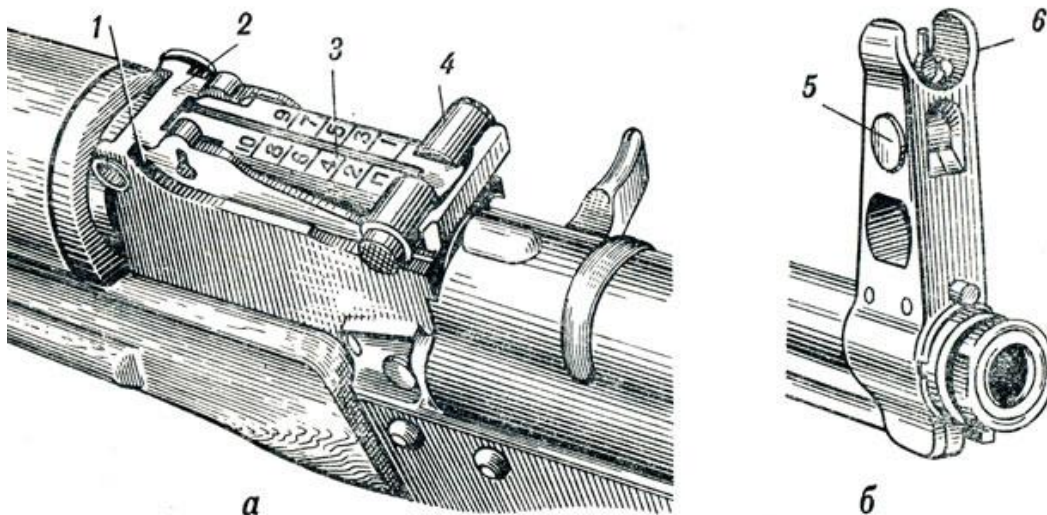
Прицельное приспособление: а - прицел; б - основание мушки; 1 - колодка прицела; 2 - пластинчатая пружина; 3 - прицельная планка; 4 - хомутик; 5 - полозок с мушкой; 6 - предохранитель мушки
